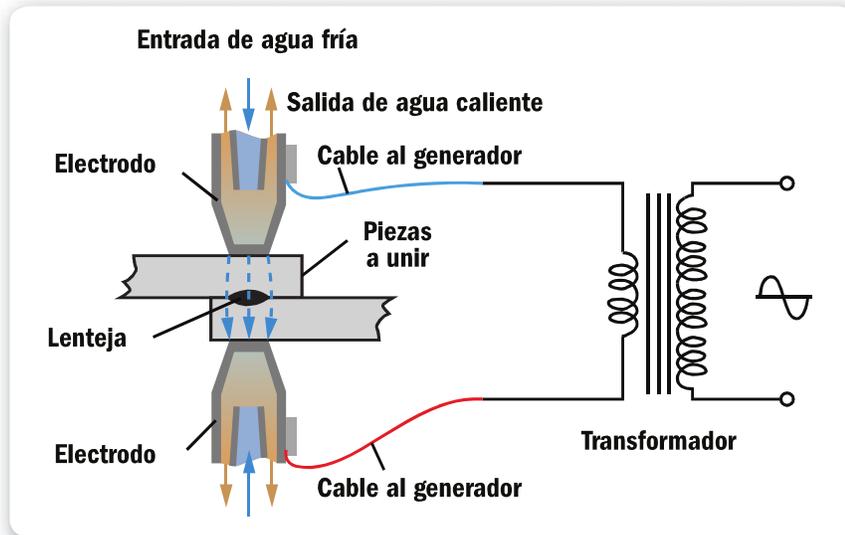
Conexión de un soldador por resistencia eléctrica.
